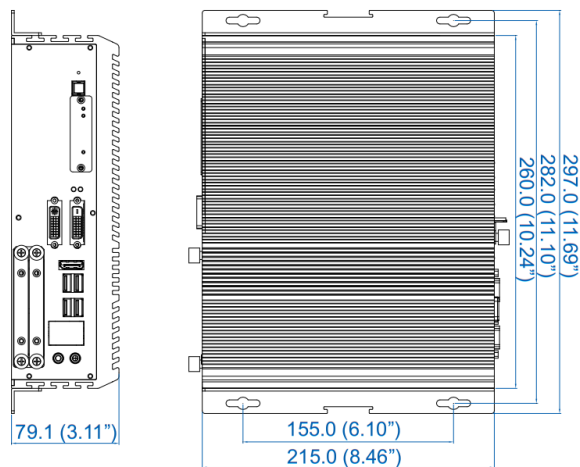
Dimensions de l'unité de contrôle et des rails de montage
